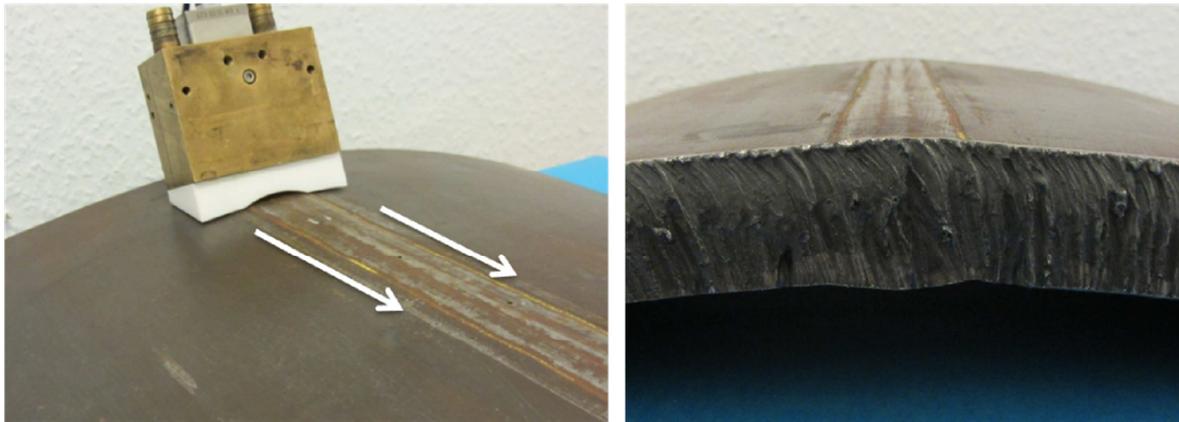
(a) Experimenteller Aufbau zur Querfehlerprüfung, (b) Schweißnahtprobe.
